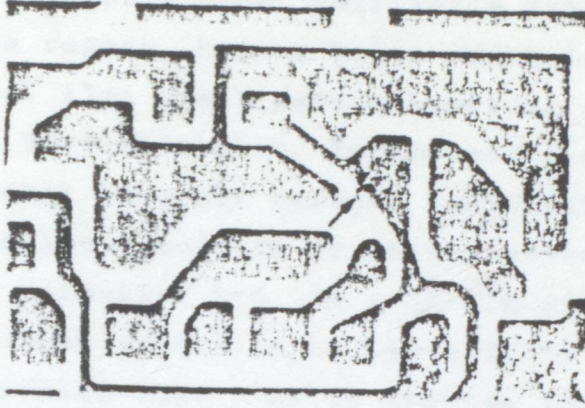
Örneklemeye boyutlarının küçültülmesinin sonuçları:(a)
